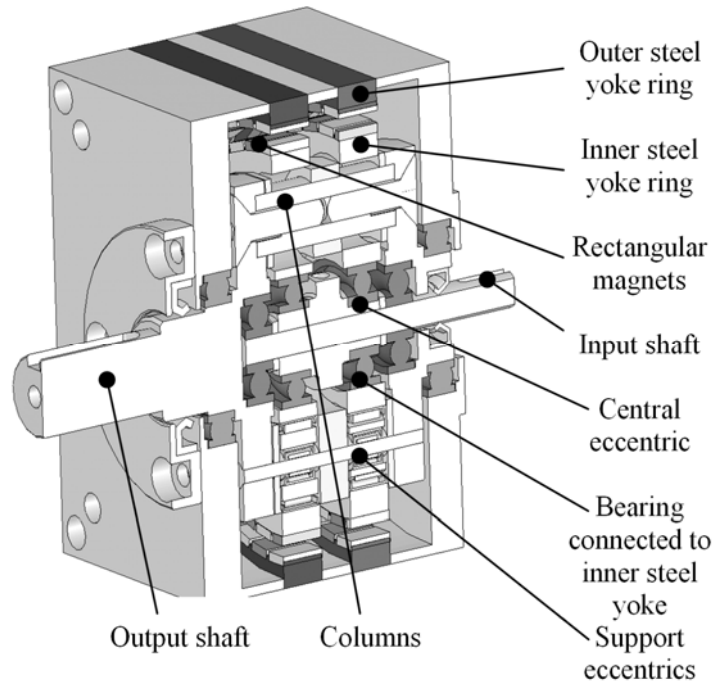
Opbygget forsøgsmodel af et simpelt magnetgear
